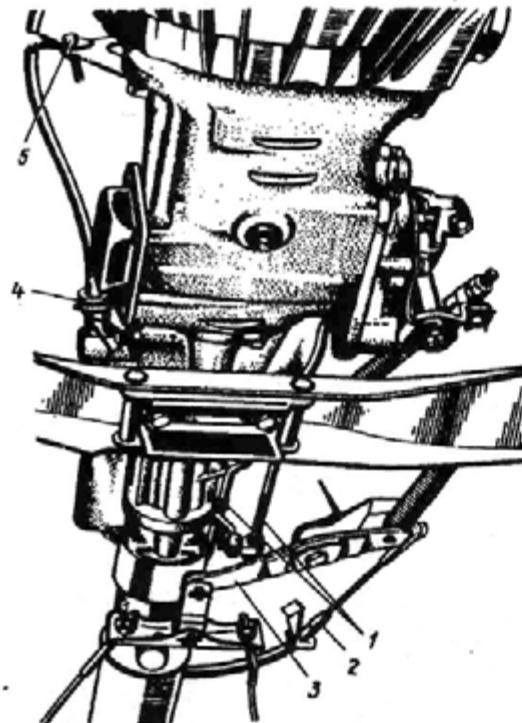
Снятие коробки передач с автомобиля (вид снизу):
